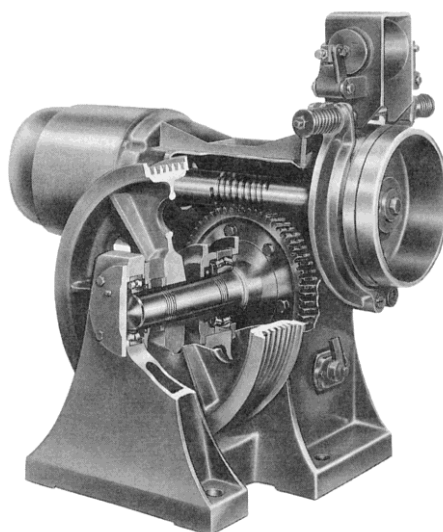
Общий вид лебедки с двухопорной схемой установки КВШ
